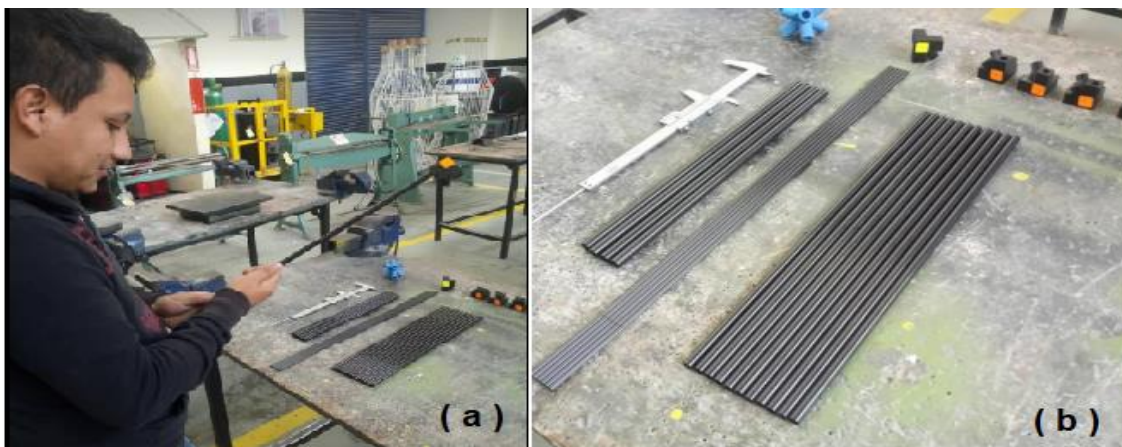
a) Preparación de los tubos b) Elementos constructivos a disposición
